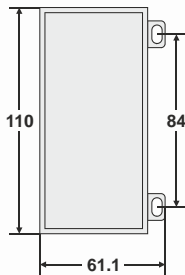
Erweiterungsmodul, Dimensionen (in mm)
